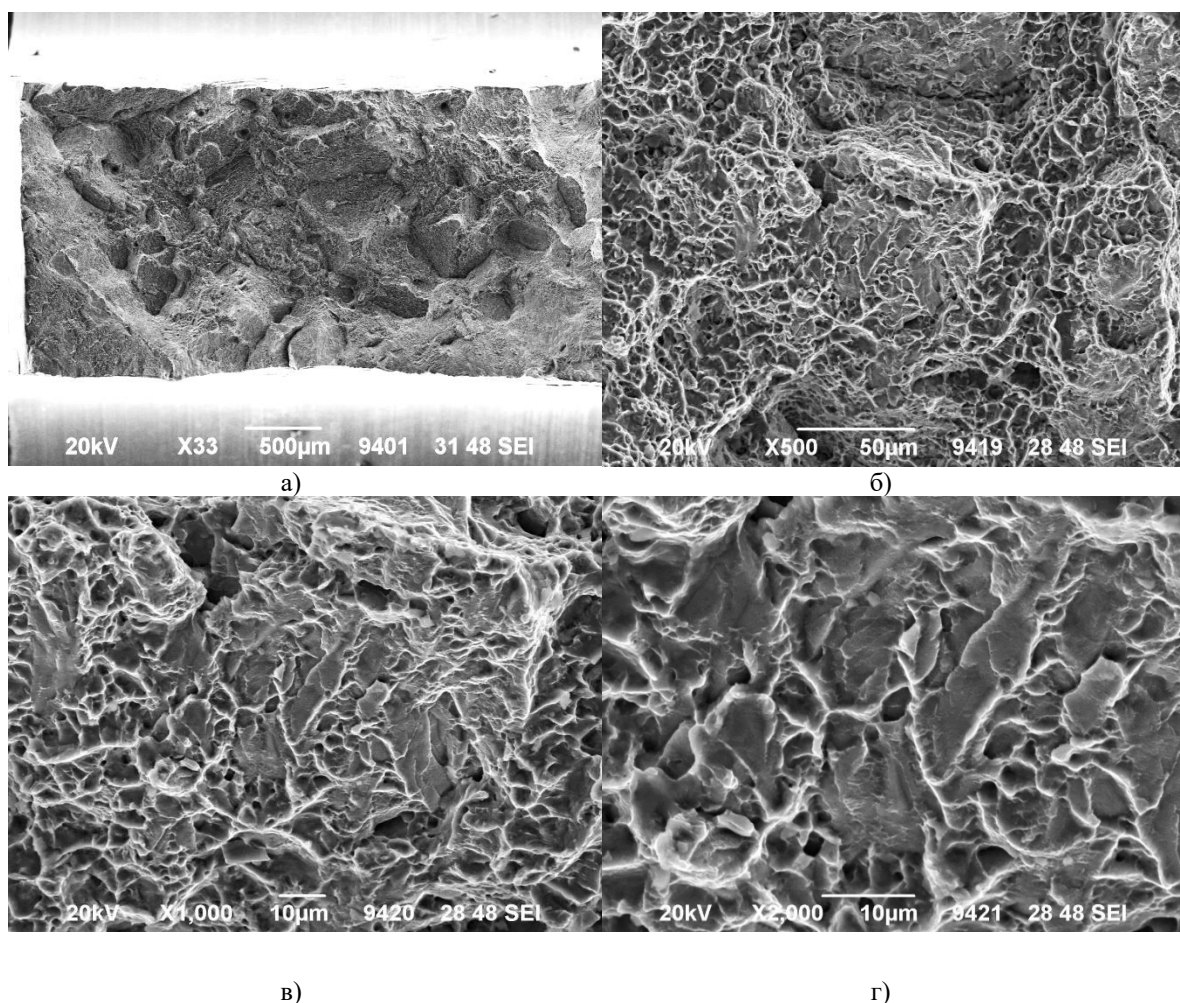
Строение излома образца сварного соединения сплава ВТ6ч после испытания на растяжение при 20 °С: а – общий вид; б-д – мелкоямочный рельеф при увеличениях x500, x1000 и x2000, соответственно
